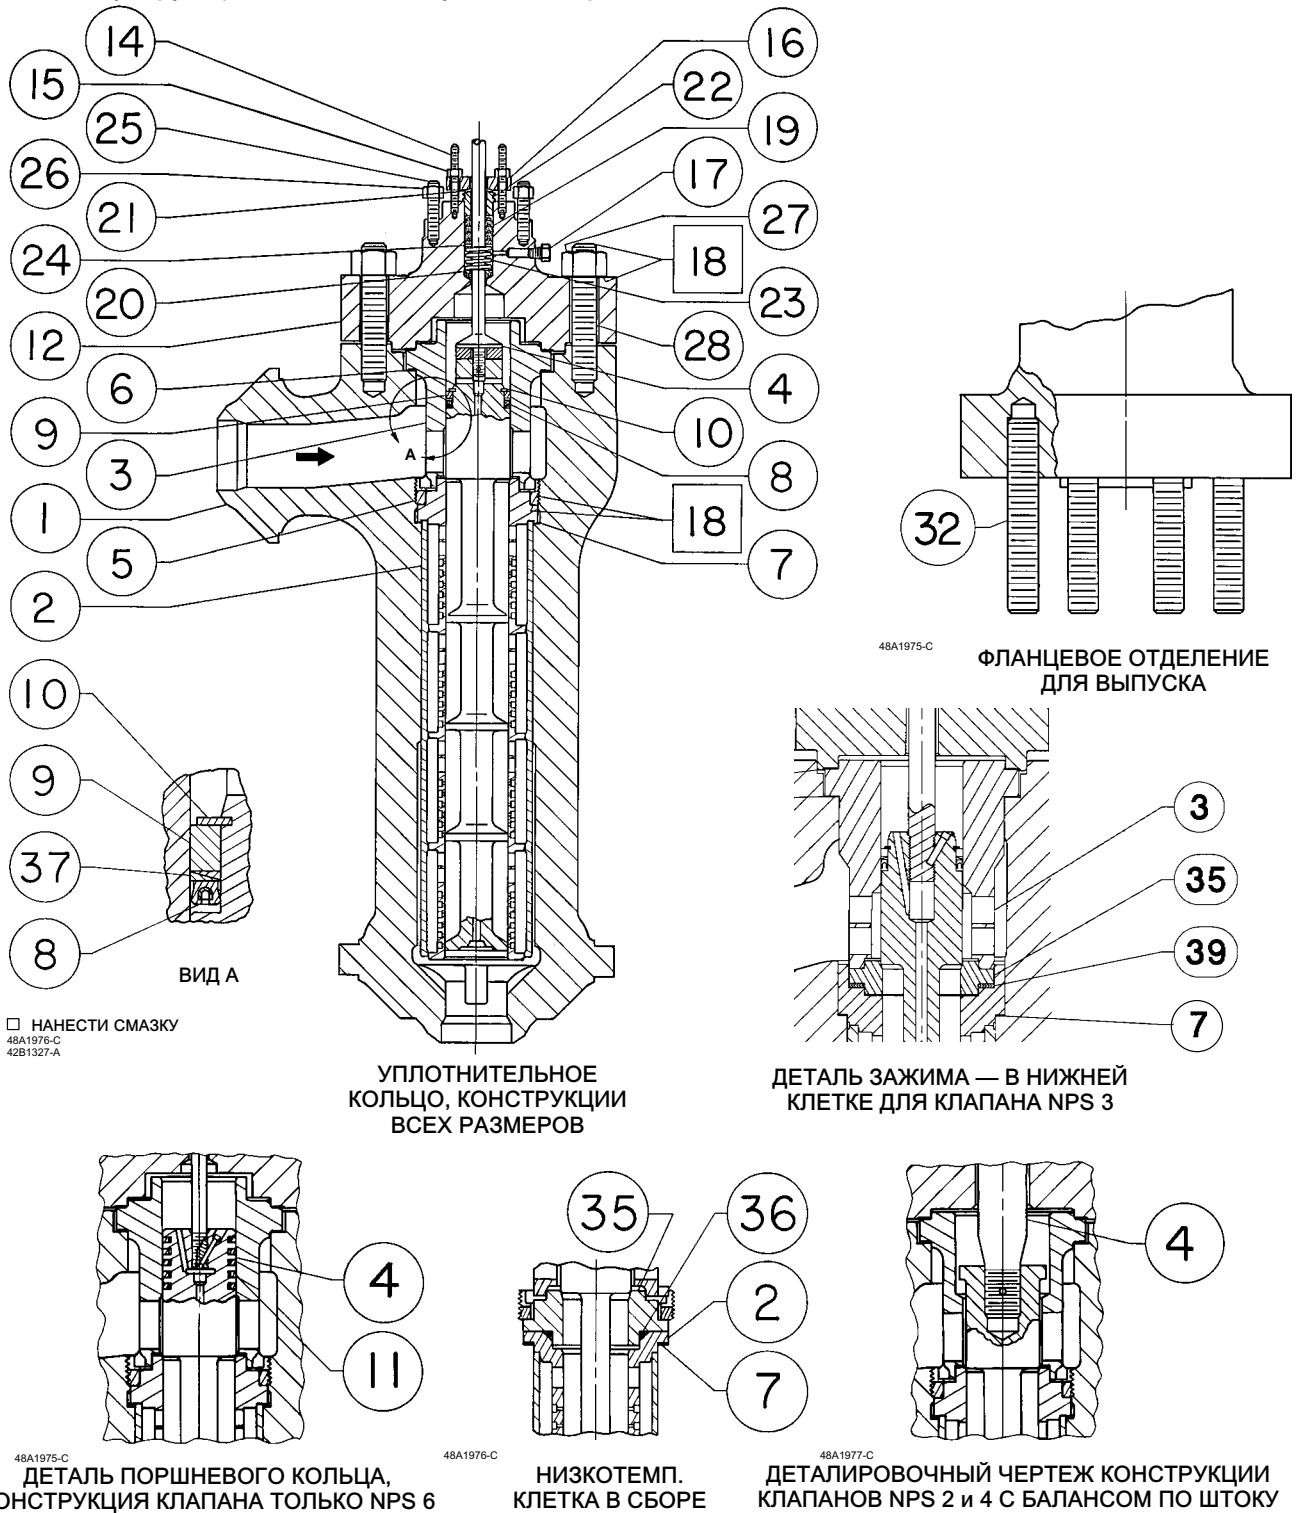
Регулирующий клапан CAV4 Fisher, шаровой NPS 2
